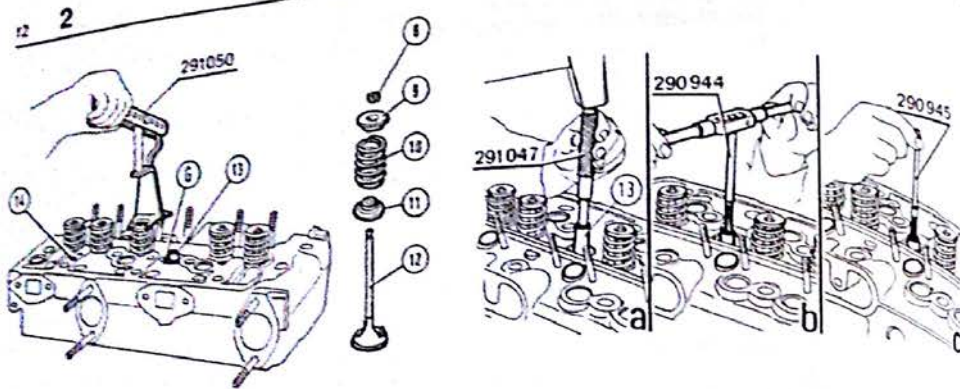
/17 - Démontage (Remontage) des ressorts et des soupapes avec l'outil 291.050.
